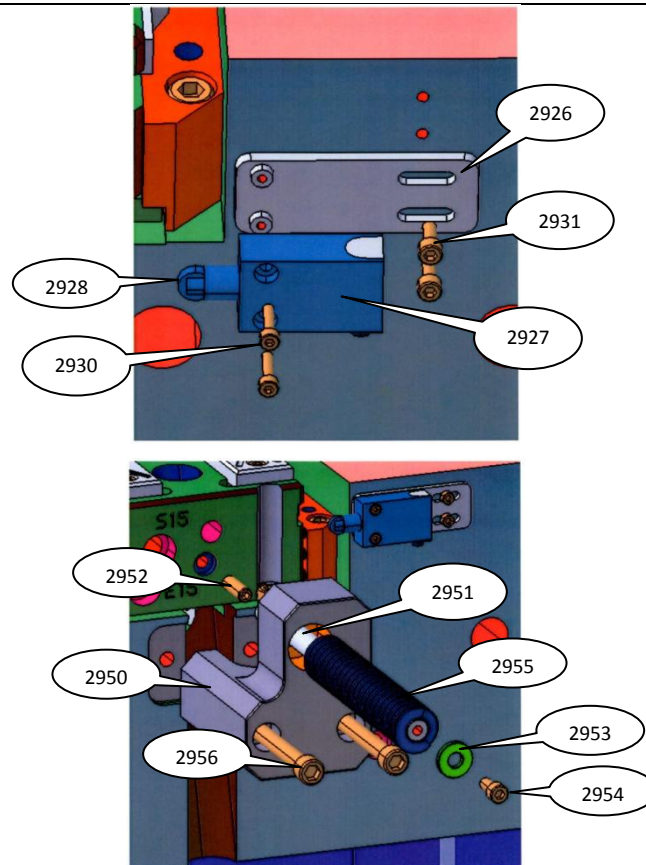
Sequência de montagem do movimento mecânico SI16.
